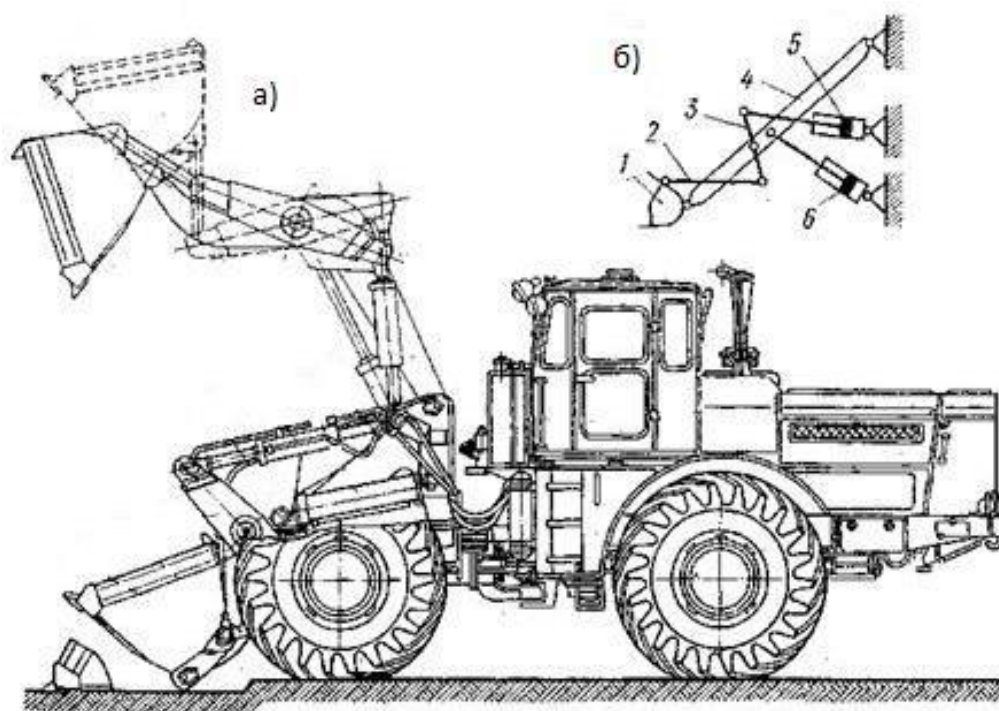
Одноковшовый фронтальный погрузчик (а) и схема его рычажно-гидравлической системы управления (б): 1 - ковш; 2,3 - рычажные механизмы; 4 - стрела; 5,6 – гидроцилиндры.
